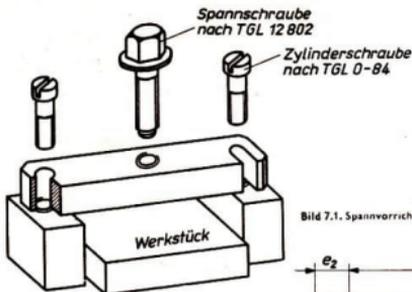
Spannvorrichtung mit Schwenklappe, Explosivdarstellung
